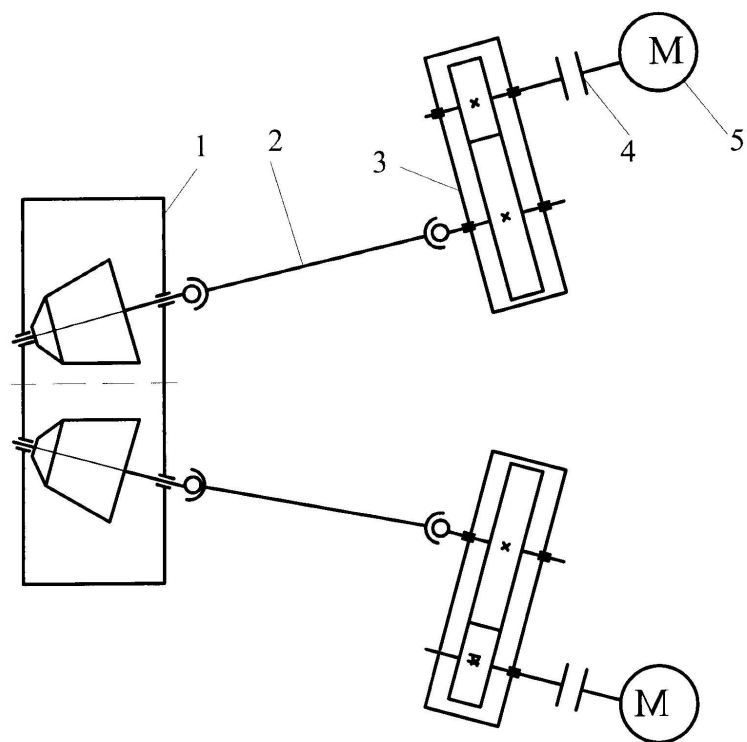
Главная линия клетки поперечно-винтовой прокатки с индивидуальным приводом грибовидных валков
